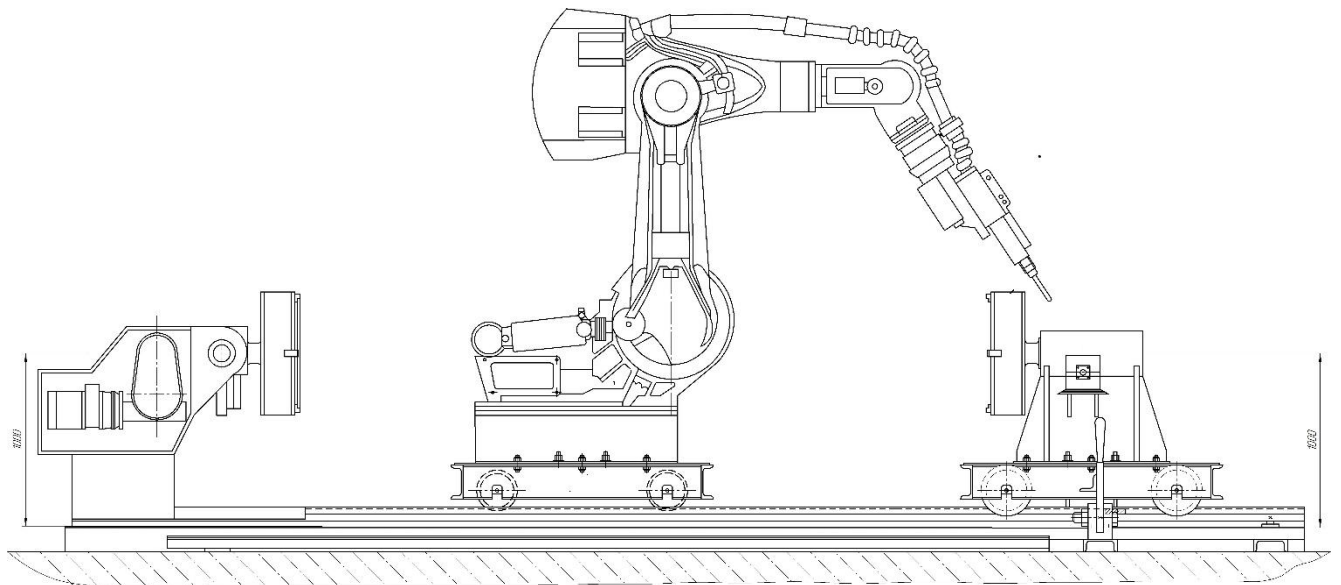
Роботизований зварювальний комплекс зварювання секцій стріли
